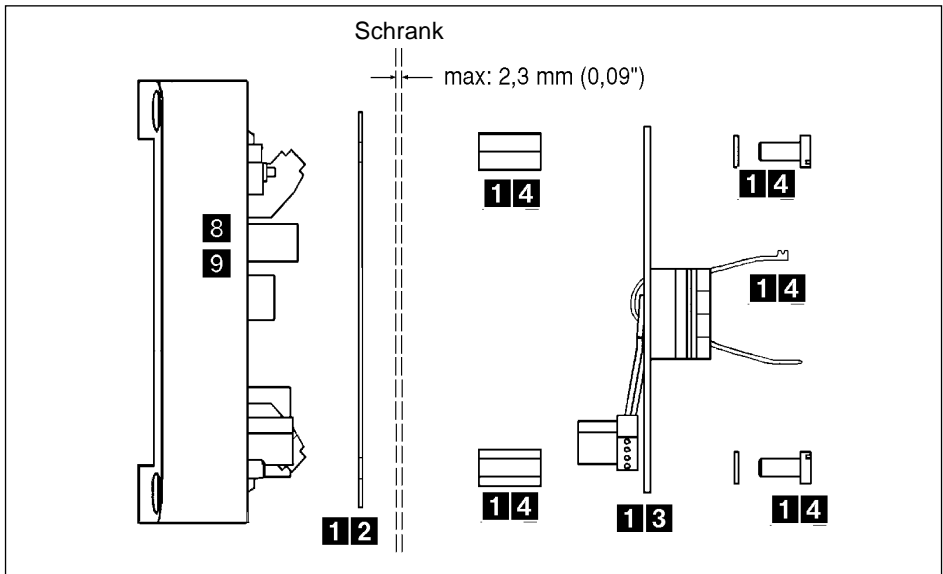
Ersatzteil Explosionszeichnung Ausführung für Schaltschrankmontage
